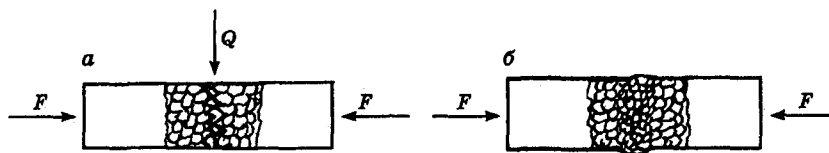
Схема образования сварного соединения при сварке давлением:
